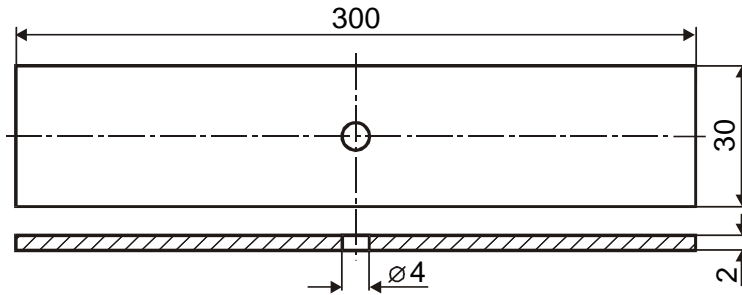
Конструкція зразка пластини із циліндричним отвором
